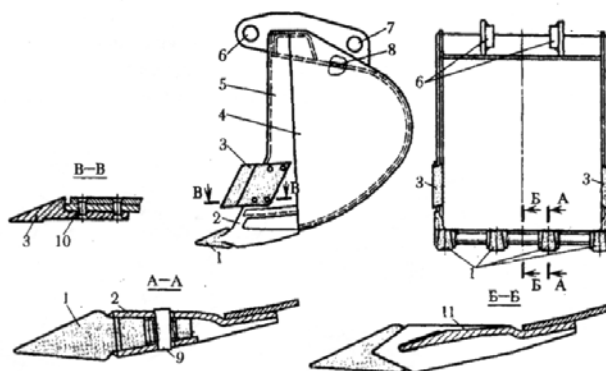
Ковш обратной лопаты экскаватора ЭО-3322Д:
